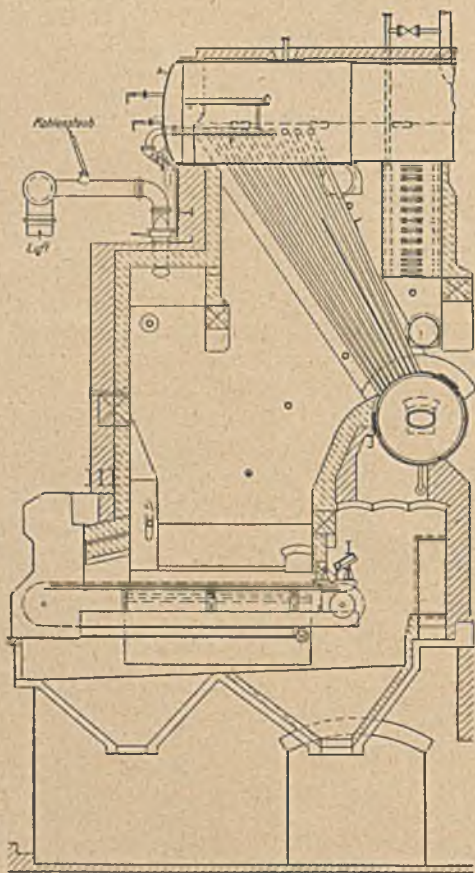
Kohlenstaubfeuerung der Maschinenbau-Anstalt Humboldt an einem Steilrohrkessel.
